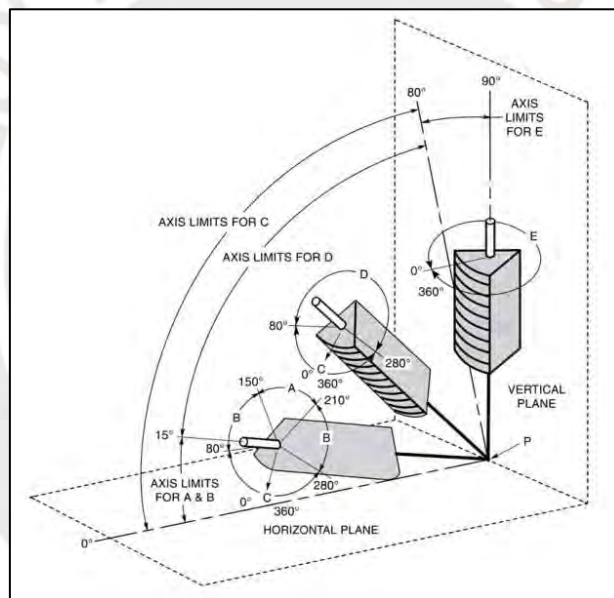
Posición relativa de los cordones de soldadura para soldadura de ranura.
